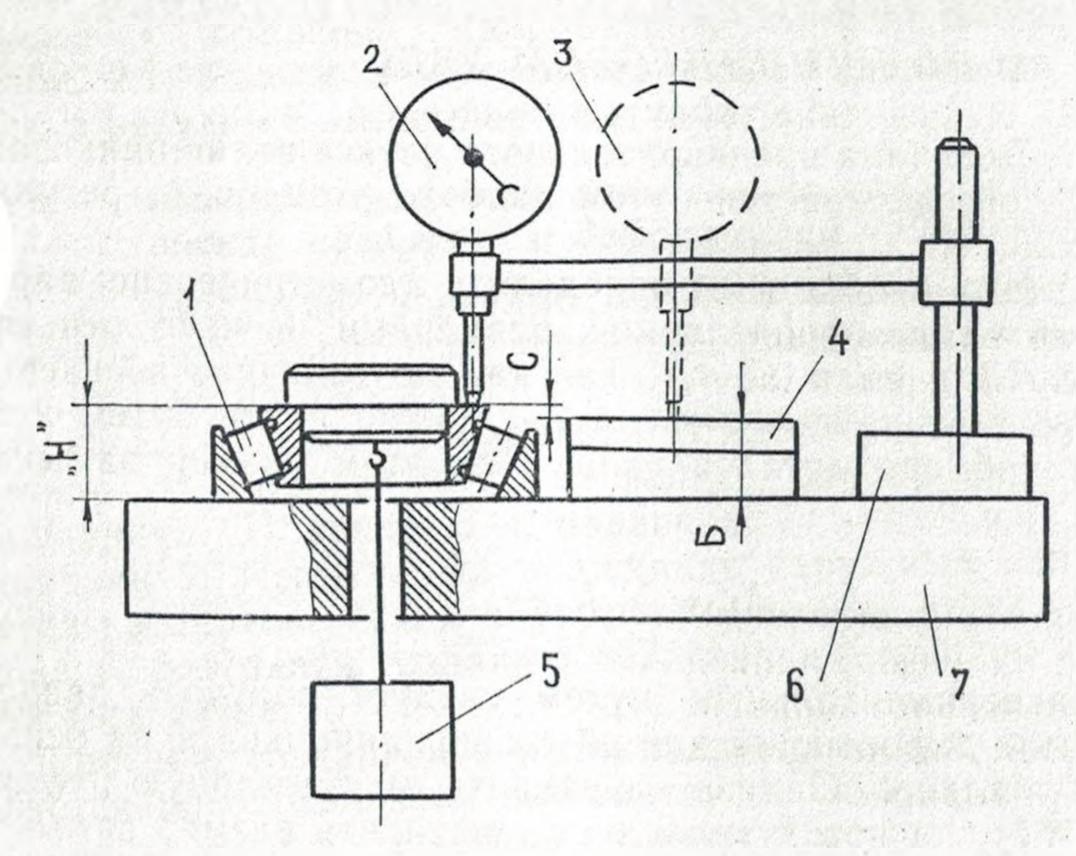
Схема определения монтажной высоты подшипника: 1 — подшипник; 2, 3 — положения индикатора; 4 — блок концевых мер; 5 — груз; 6 — магнитная индикаторная стойка; 7 — опора приспособления
